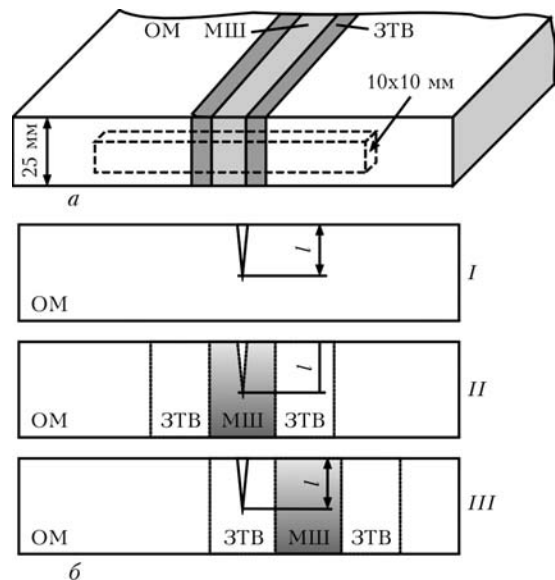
Схема зварного з'єднання з високоміцної сталі RQT601 та вирізки балкових зразків (а) і балкові зразки для випробовувань на тріщиностійкість компонентів зварного з'єднання (б); I — основний метал (ОМ); II — метал шва (МШ); III — ЗТВ
